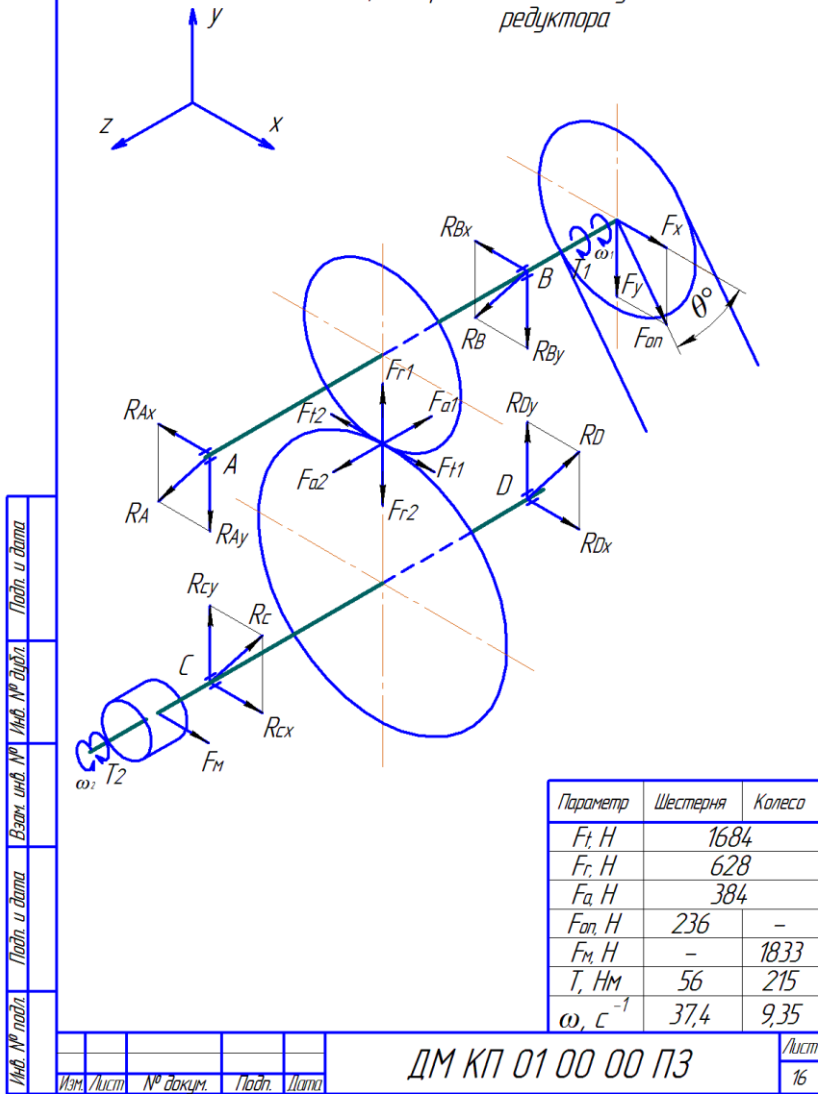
Пример схемы нагружения валов цилиндрического одноступенчатого редуктора с муфтой и ременной передачей
